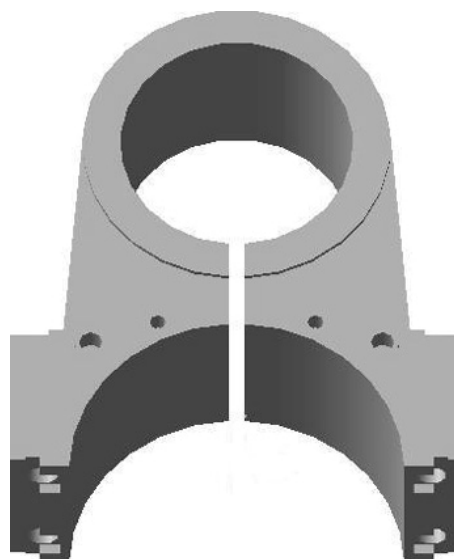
Зовнішній вигляд шатуна преса з механічною обробкою тріщини, що утворилася, під зварювання
